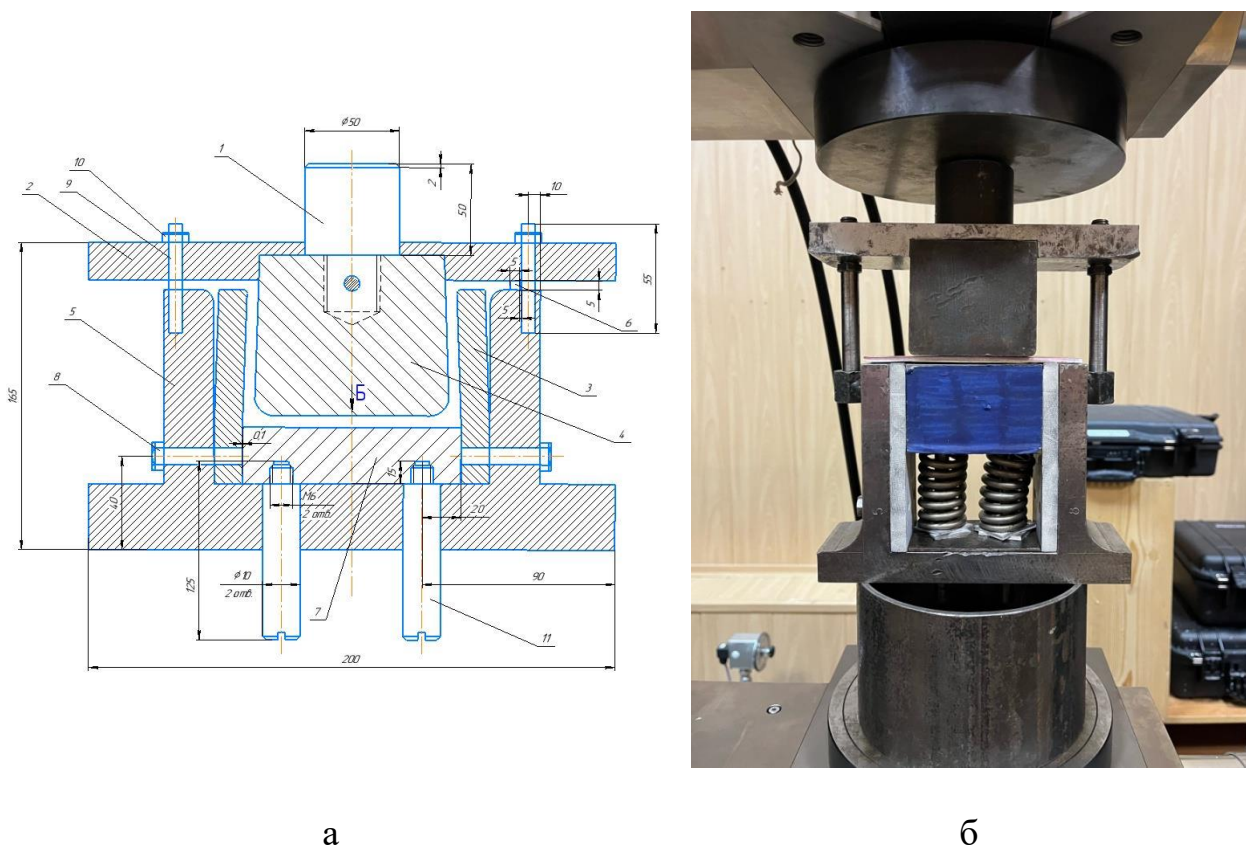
Схема штамповой оснастки (а) и экспериментальный штамп (б): 1 – хвостовик; 2 – верхняя плита; 3 – упругие планки; 4 – пуансон; 5 – матрица и нижняя плита; 6 – упор; 7 – выталкиватель; 8 – болт для крепление планок, 9 - направляющий болт; 10 – болт 11 – направляющие выталкивателя.
